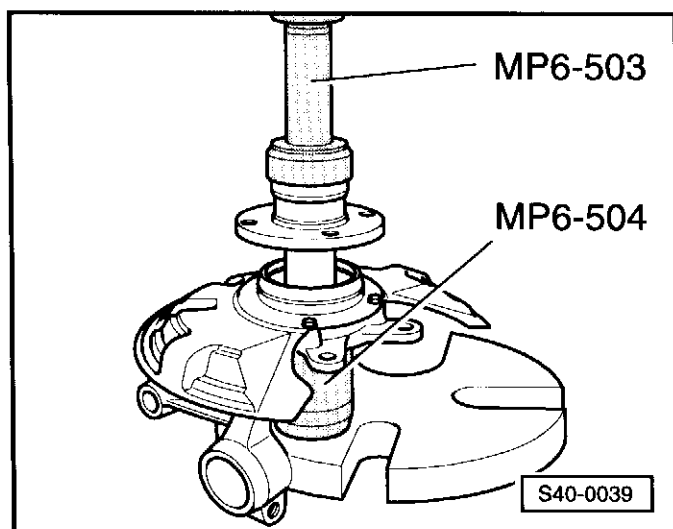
Выпрессовка подшипника из крышки подшипника ступицы колеса
